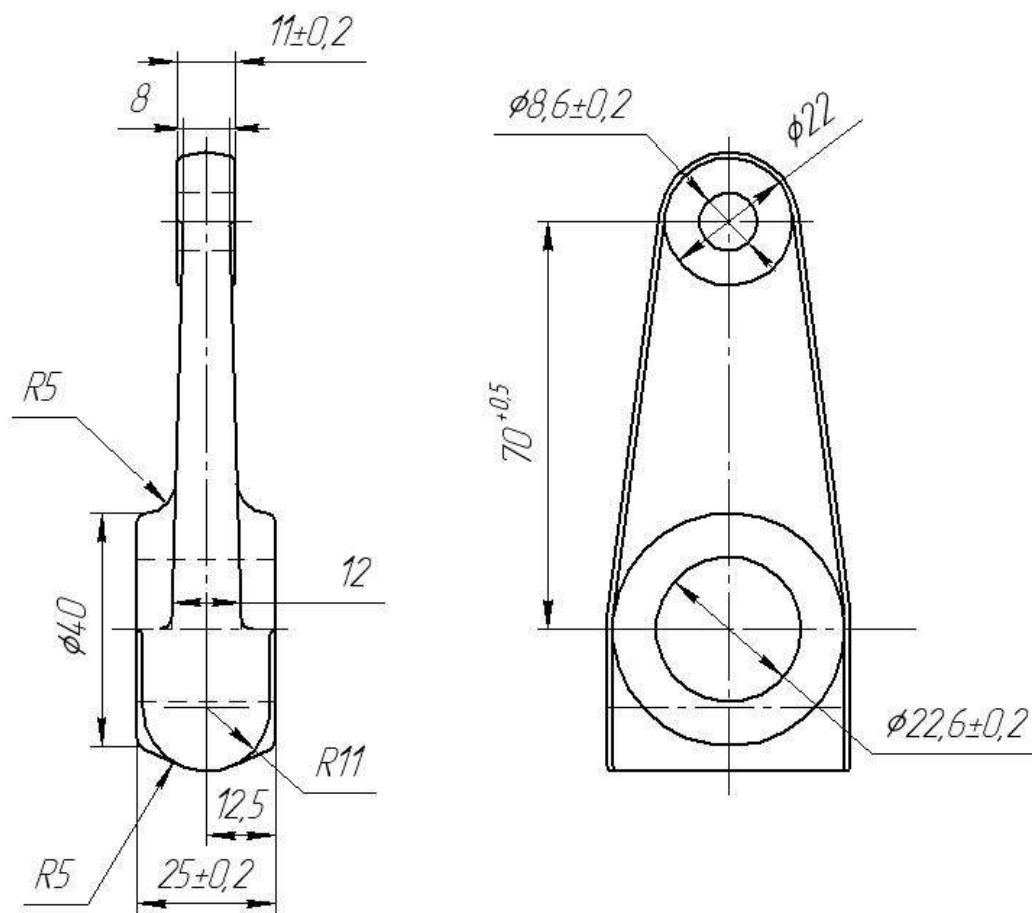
Креслення заготовки важеля приводу ручного гальма
